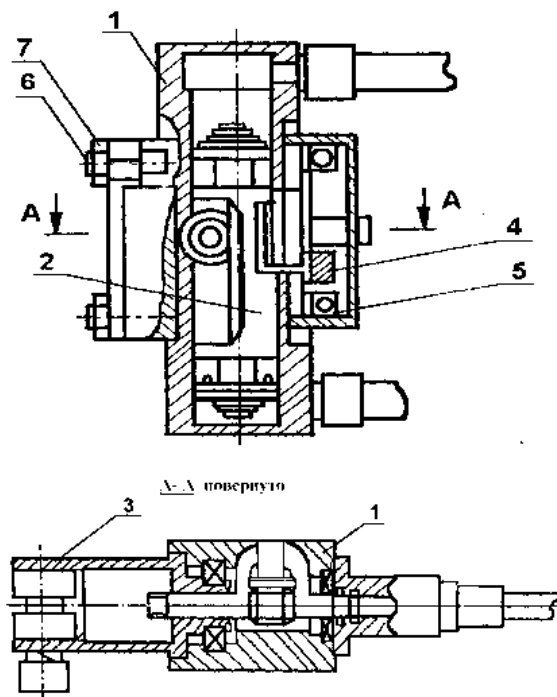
Модуль ротації схвата: 1 – корпус; 2 – шток-рейка; 3 – вал-шестерня;
